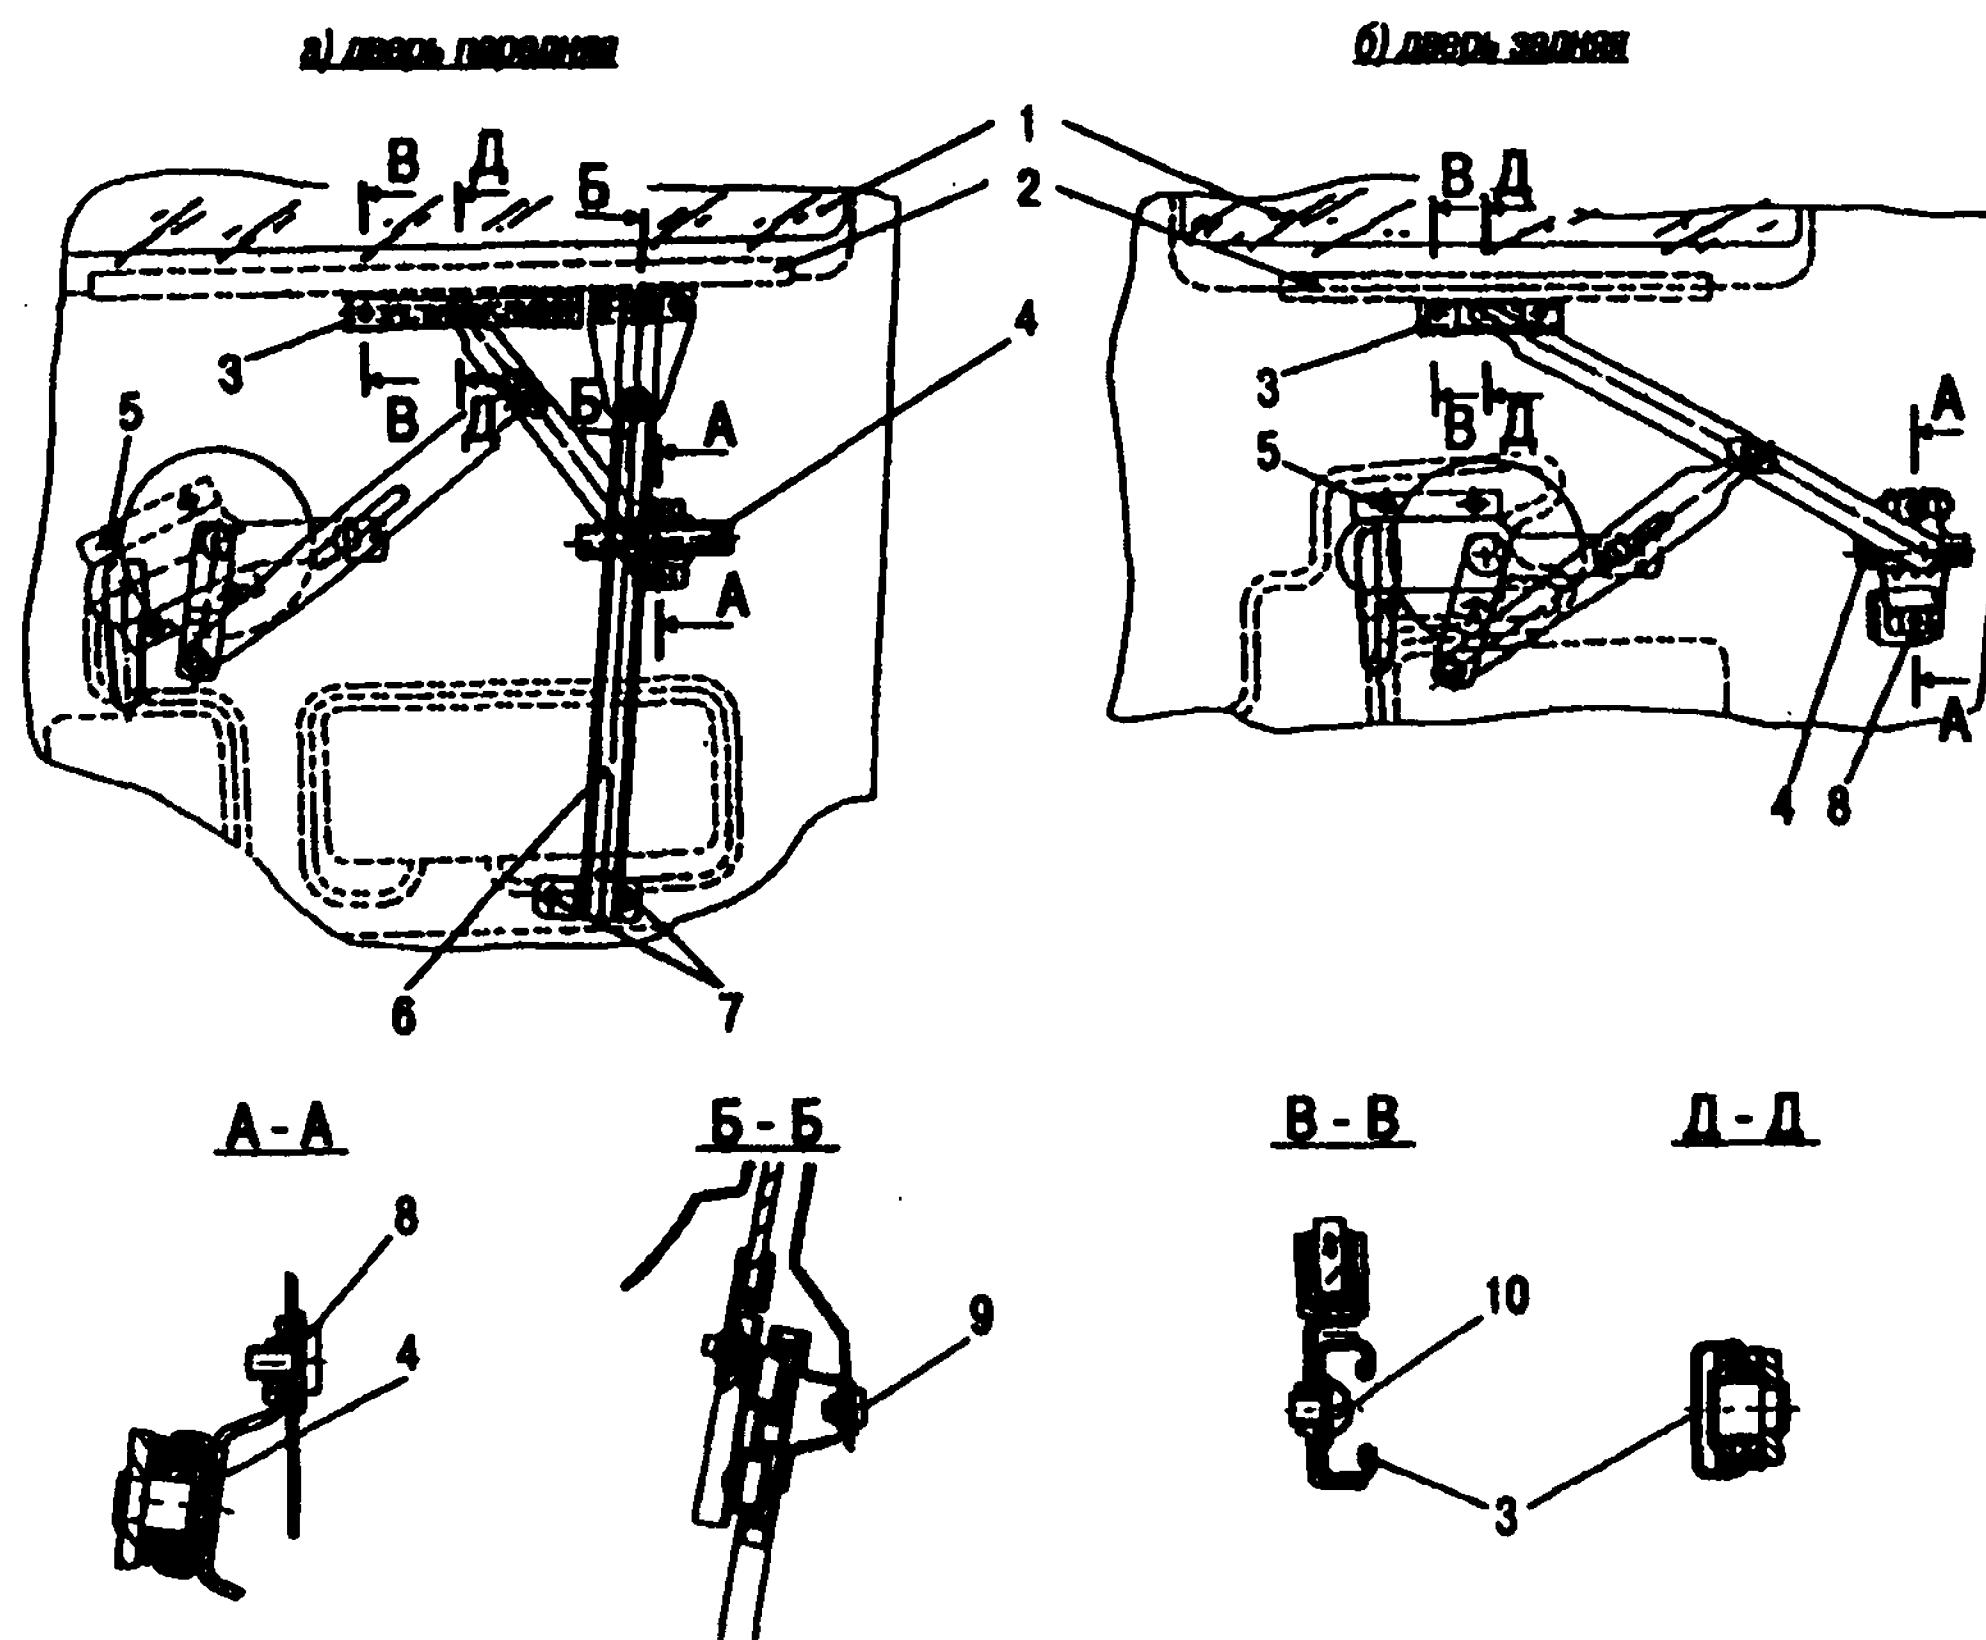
Установка стеклоподъемников дверей: 1 - стекло опускаемое с обоймой в сборе; 2-обойма стекла; 3 - верхняя кулиса; 4 - нижняя кулиса; 5 - винт крепления корпуса стеклоподъемника; 6 - направляющая стеклоподъемника; 7 - болты крепления направляющей стеклоподъемника; 8 - винты крепления нижней кулисы; 9 - болты крепления направляющей верхней; 10 - винты крепления верхней кулисы
